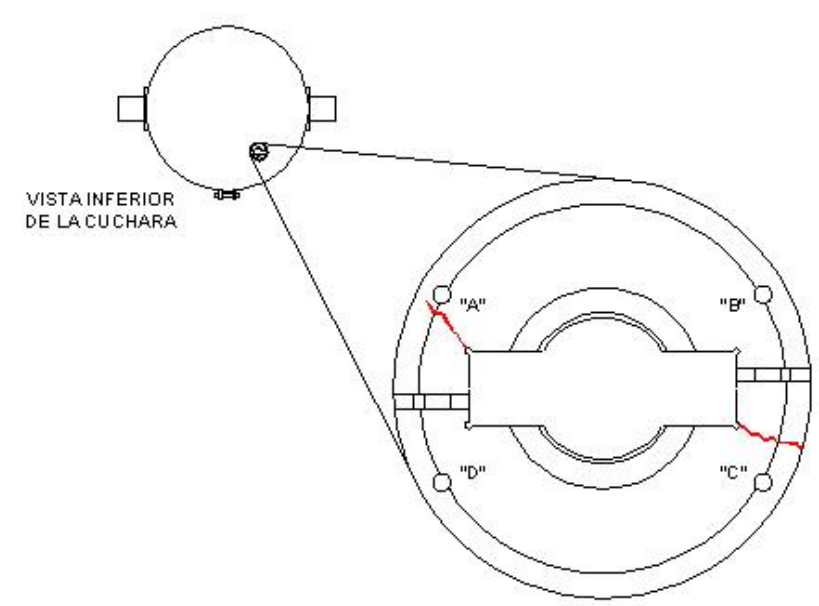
Croquis de las fisuras aparecidas en las placas bases, vistas desde el fondo de las cucharas
